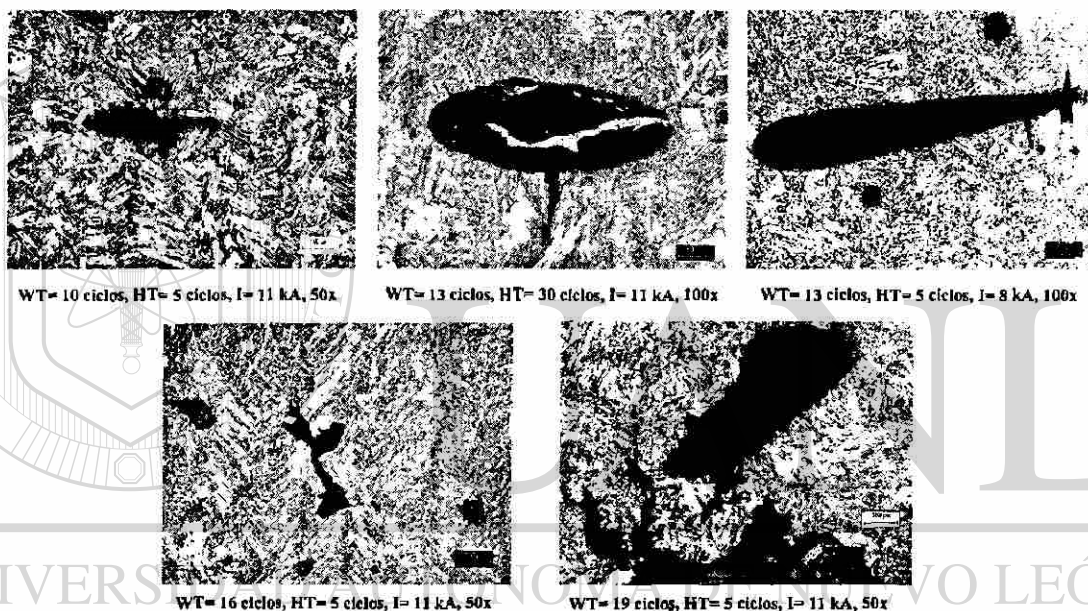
Porosidades en núcleos de soldadura a diferentes condiciones de prueba.
